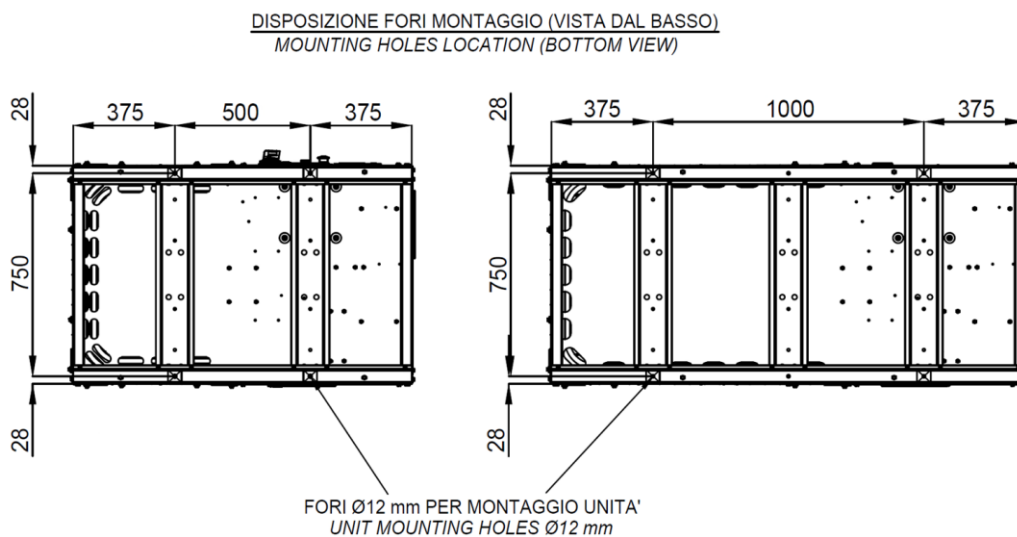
Ubicación de los orificios de montaje (vista inferior)
